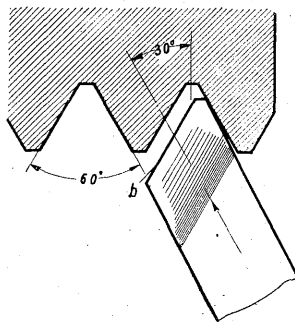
Ustawienie noża i górnych sań tokarki przy skrawaniu gwintu.
